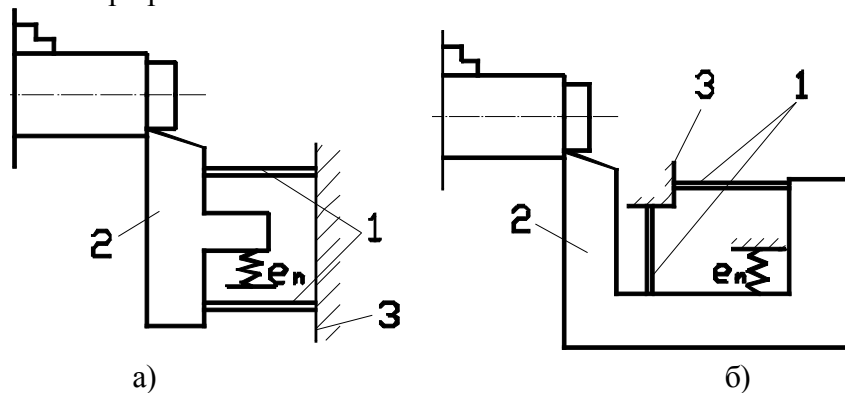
Схеми токарної обробки різцетримачами з паралельними (а) та перпендикулярними (б) пружними пластинами, де: 1 – пружні пластини; 2 – віджимна частина з різцем; 3 – корпус різцетримача, що закріплений в револьверній головці; e_n – податливість приводу позиціонування віджимної частини
